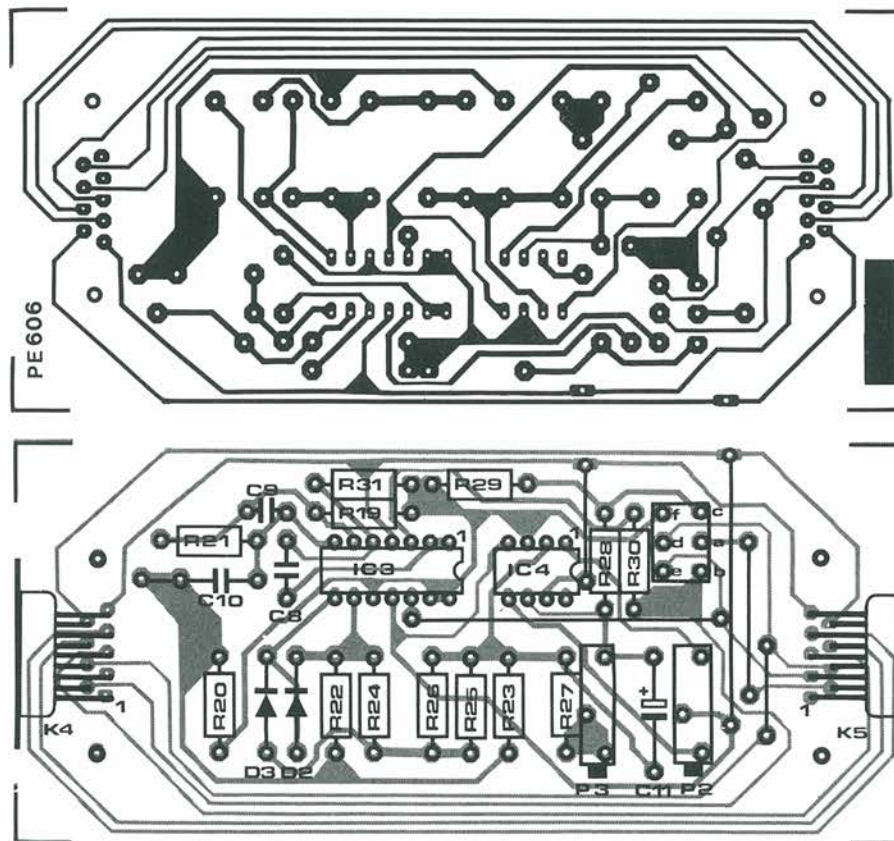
Circuito stampato e disposizione dei componenti sul circuito stampato del rettificatore.
